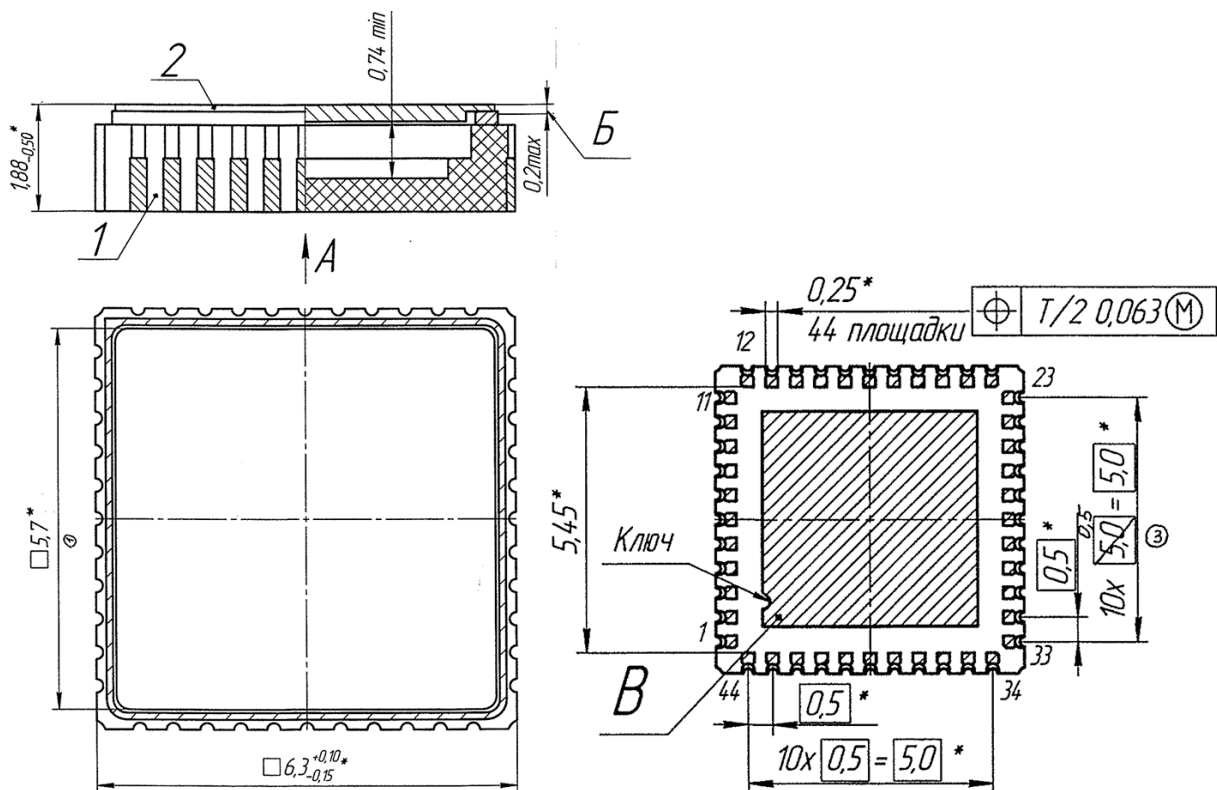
Габаритный чертеж корпуса МК 5165.44-1 (размеры в мм)
